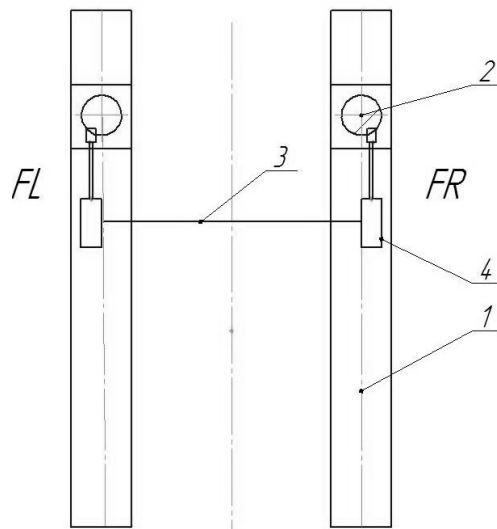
Схема взаємного калібрування головок FL-FR. Перший крок: 1 – підйомник; 2 – рухомий майданчик для керування коліс; 3 – калібрувальний пристрій; 4 – вимірювальна головка
